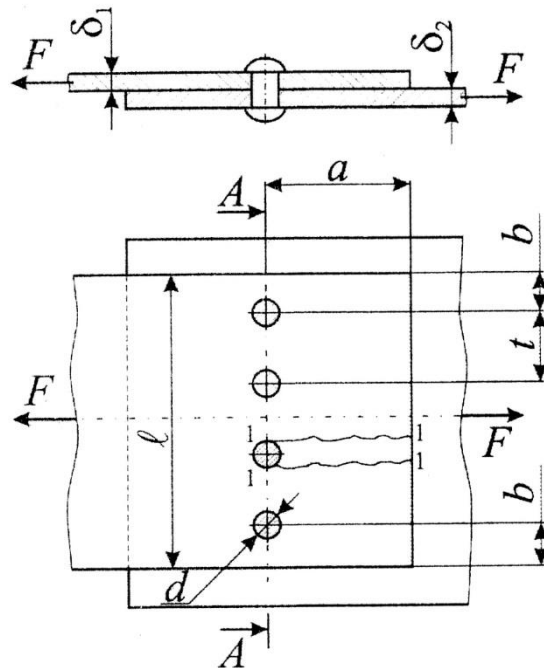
Схема до розрахунку заклепкового з'єднання
